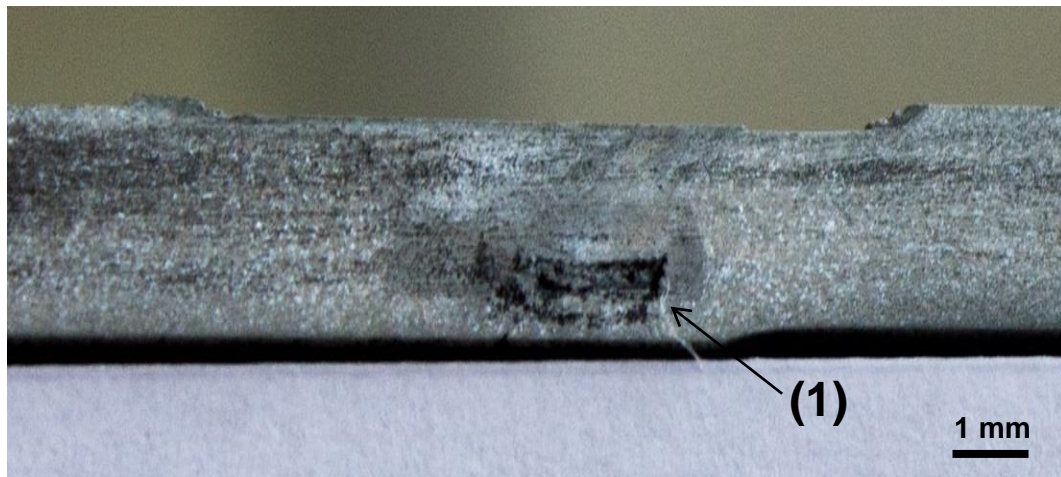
Seção da junta soldada com descida de 2,3mm da ferramenta.
